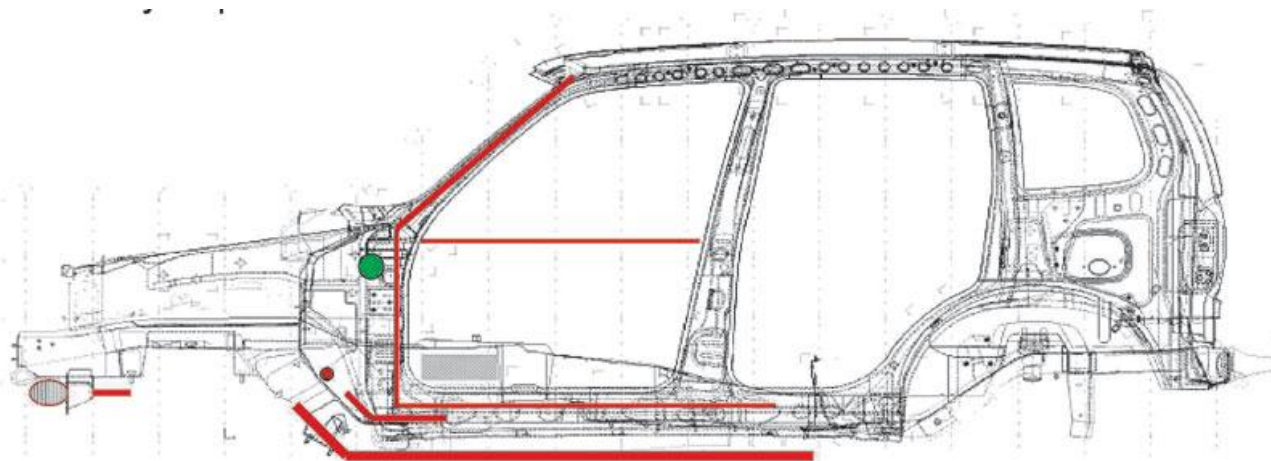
Сварные соединения передних частей кузова Chevrolet NIVA
